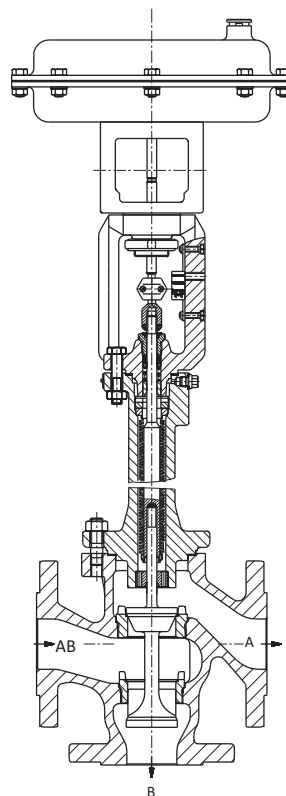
· Пневматический регулирующий распределительный вариант клапана тип 3244-7 с дополнительным сильфонным и приводом тип 3277.
